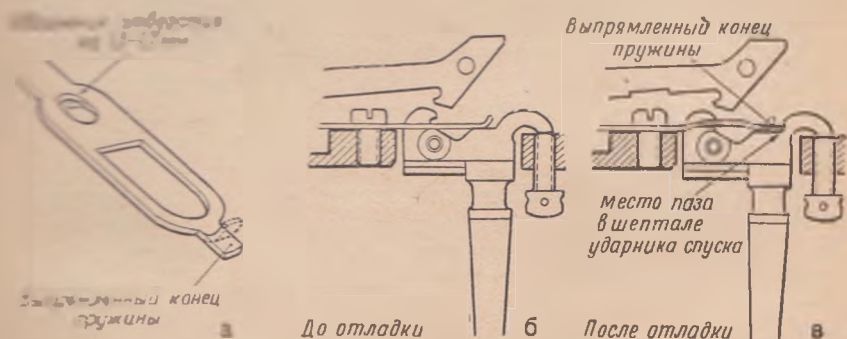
Обработка деталей спускового механизма для устранения «провала» спицы спуска
